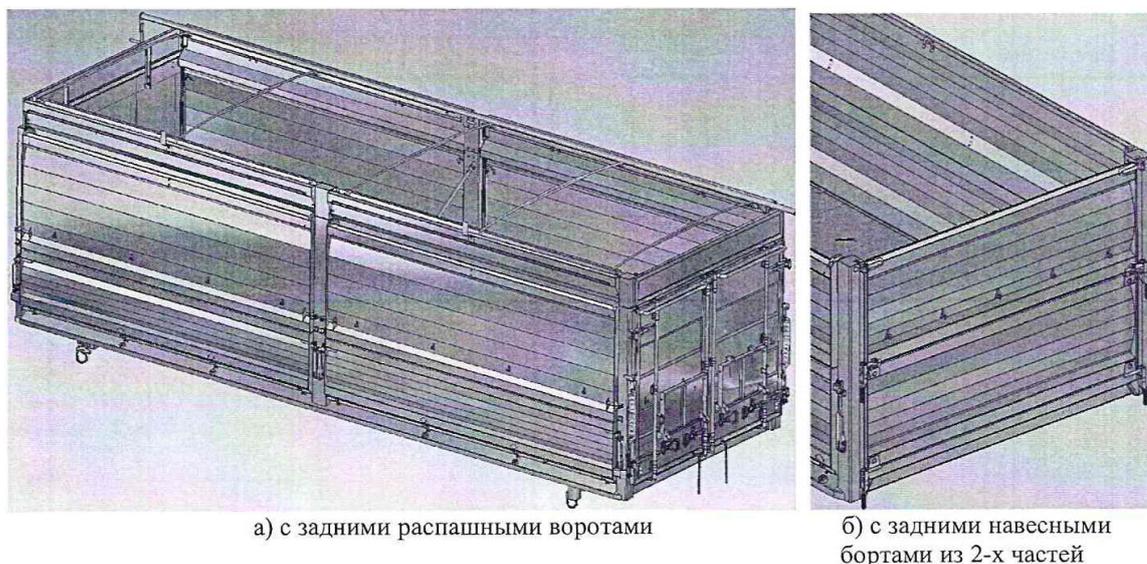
Платформа 7200 с двумя боковыми нижними бортами.
